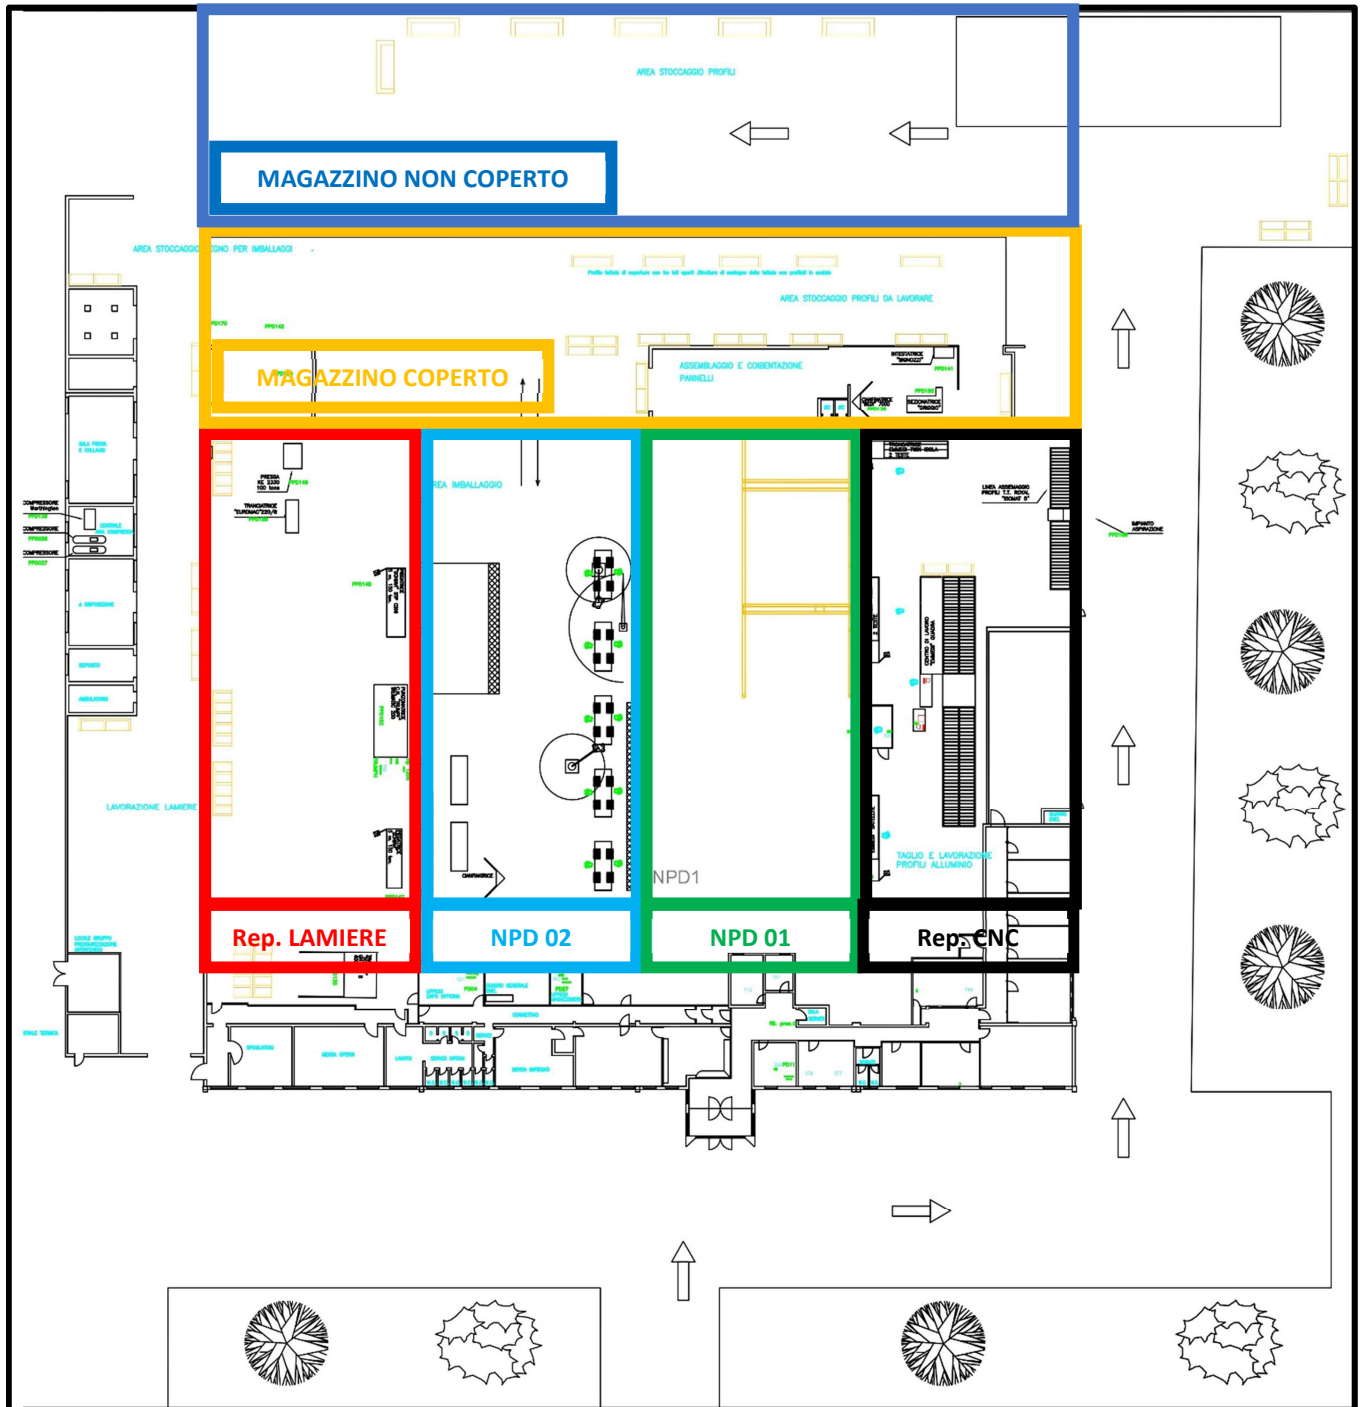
Layout stabilimento AZA a Noventa Padovana (PD)
